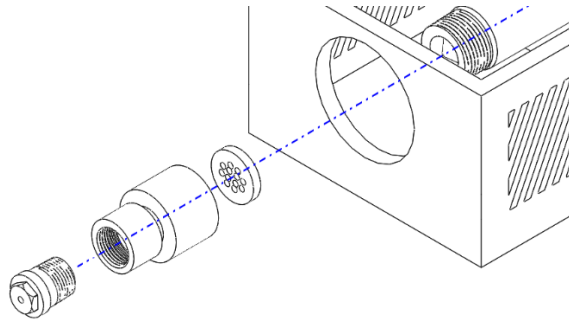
Ensamble de la boquilla, cabezal, plato rompedor y cilindro
